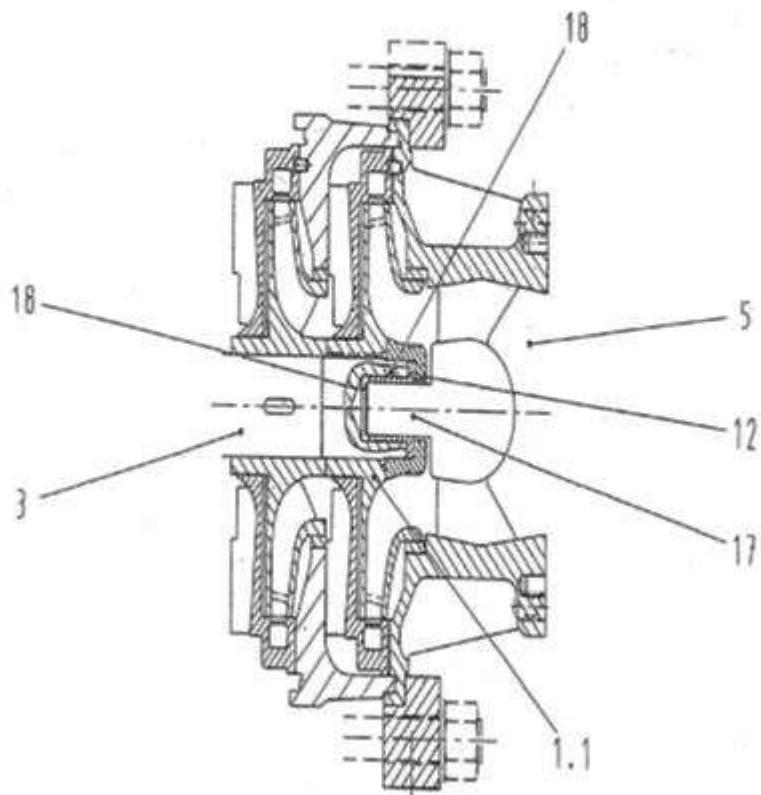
Частичный вид в разрезе, показывающий подшипниковый узел со стороны всасывания [2]
